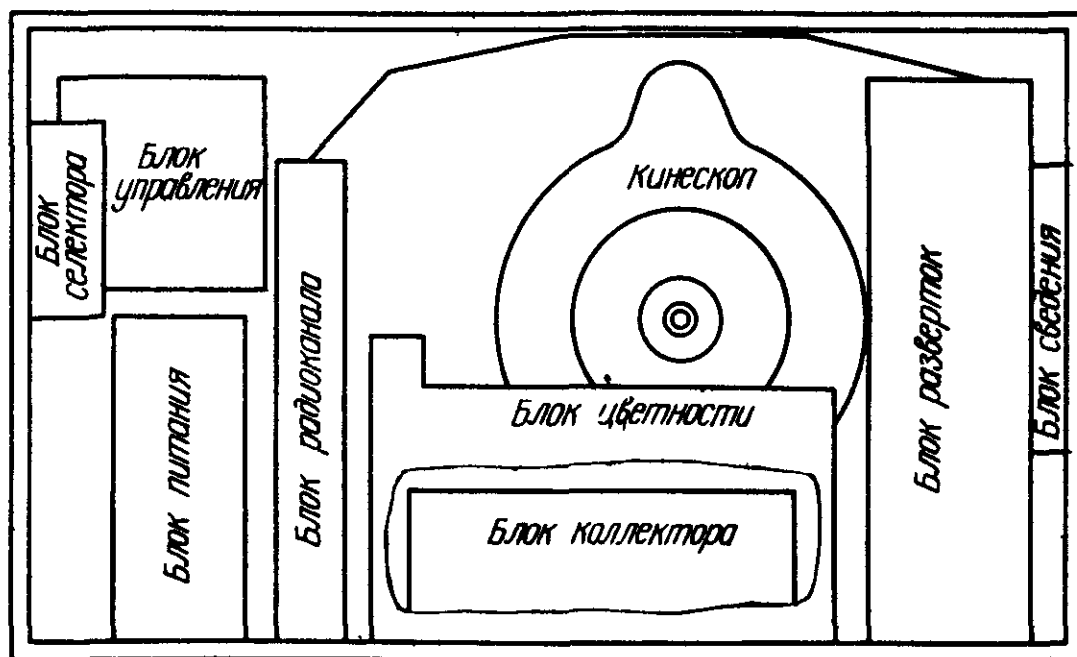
Расположение блоков в телевизоре (вид со стороны задней стенки)
